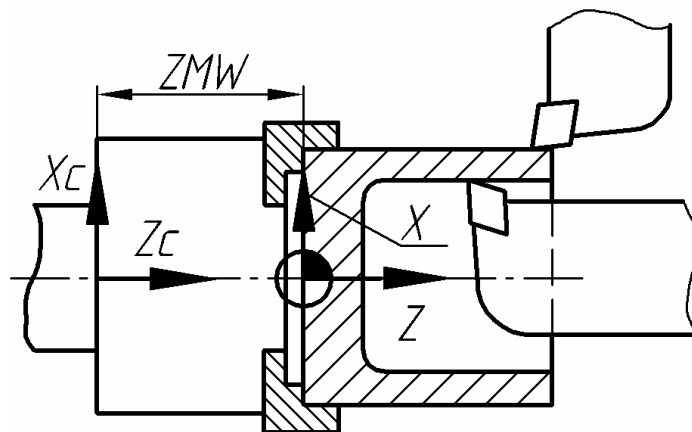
Смещение нулевой точки обрабатываемой детали
